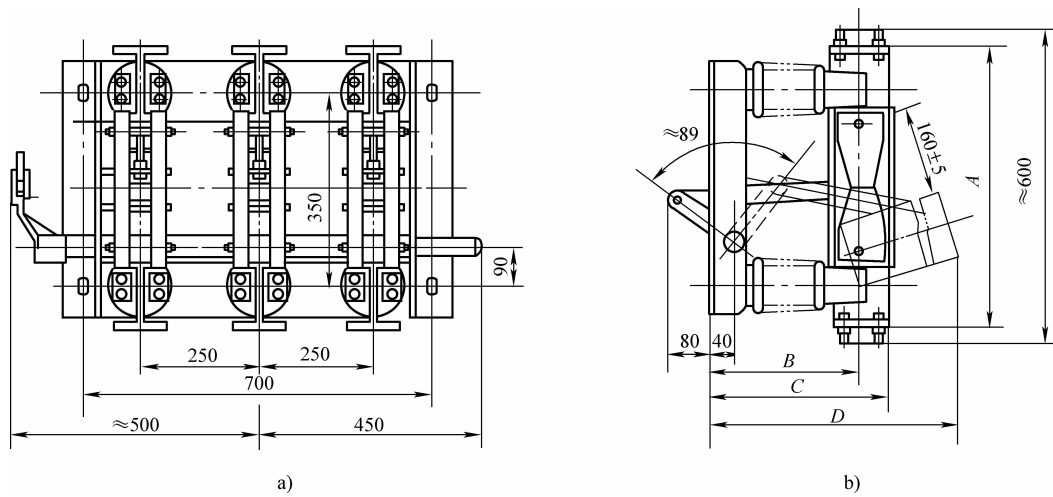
GN22-10 型隔离开关的外形结构及安装尺寸
